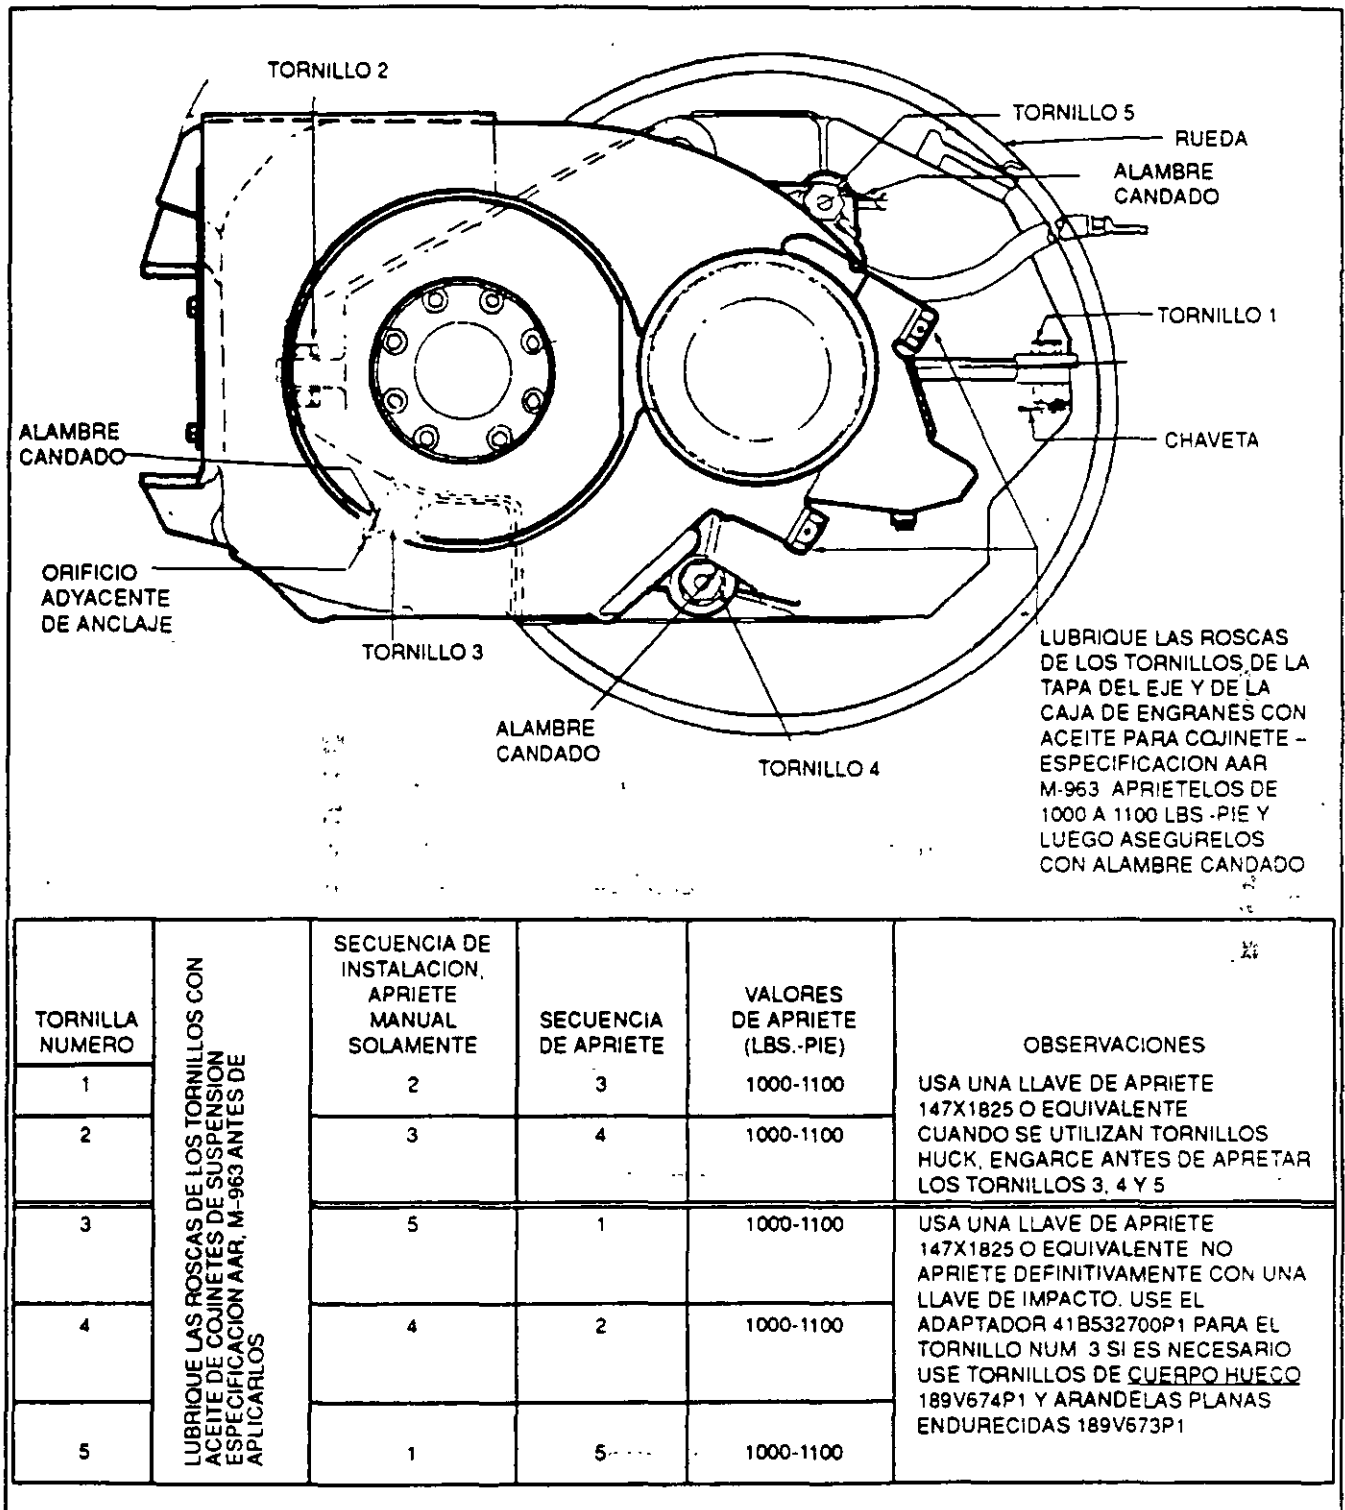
MONTAJE DE LA TAPA DEL EJE Y LA CAJA DE ENGRANES GE752E8 E-29368B-S
